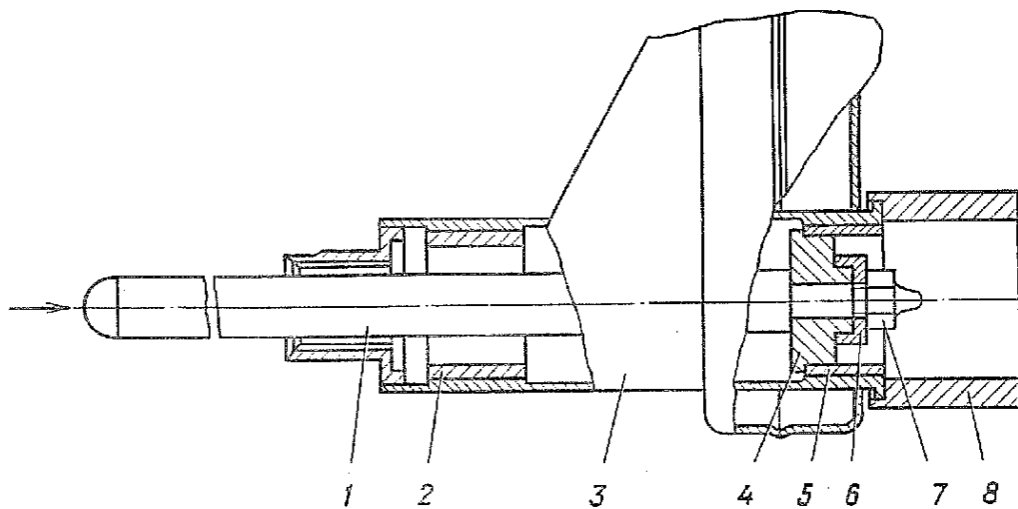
Выпрессовка внутренней втулки рычага подвески:
